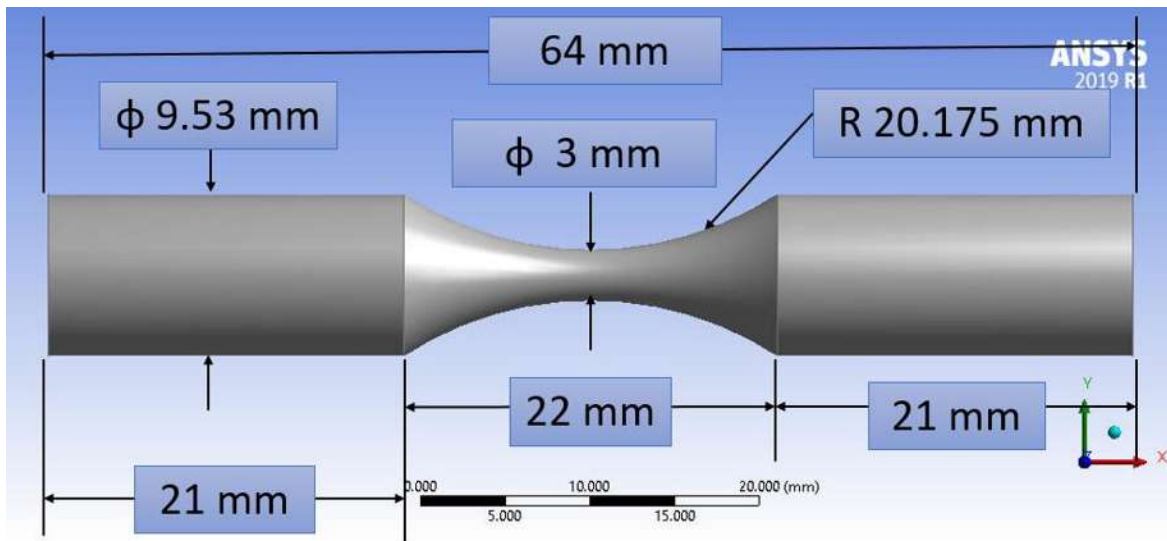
Dimensiones de la probeta de acero maraging 300.
